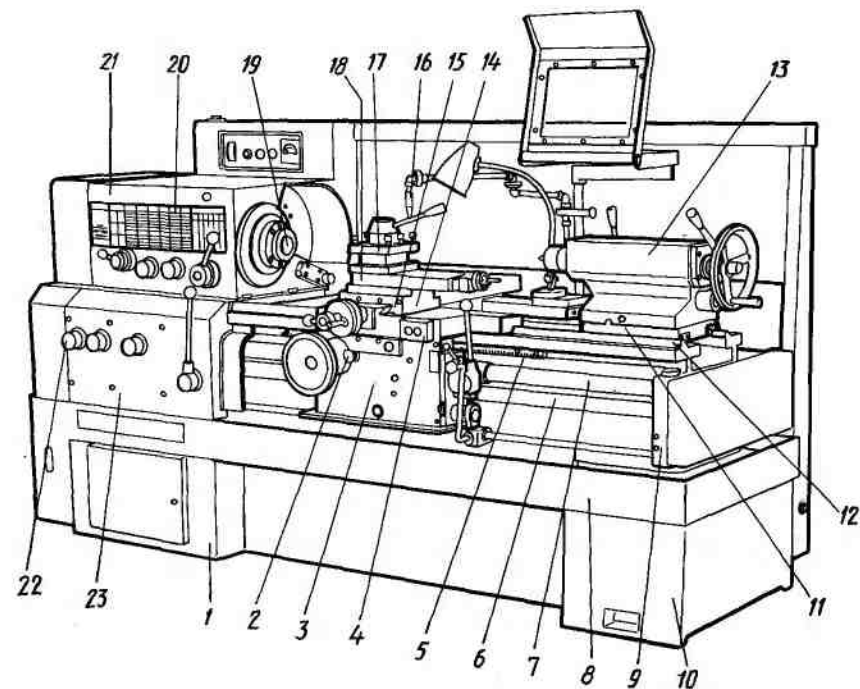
Основные сборочные единицы токарно-винторезного станка мод. 16К20:
